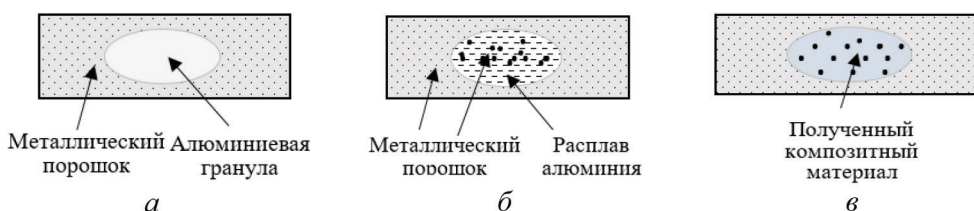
Схема получения ММКМ: а — общий вид заготовки ММКМ в пресс-форме; б — в процессе прессования; в — полученный образец ММКМ
